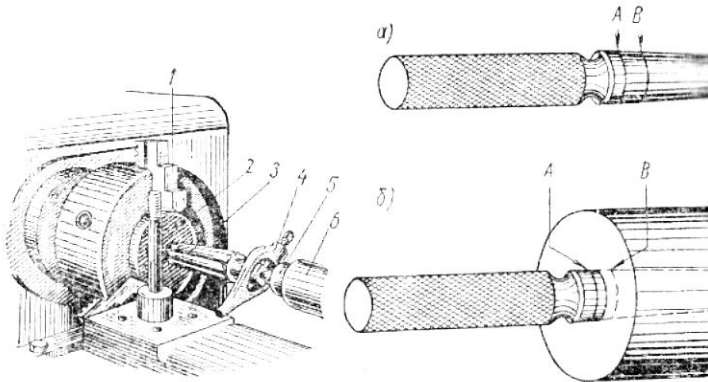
Схема установки развёртки на токарном станке и проверка конического отверстия калибром-пробкой
